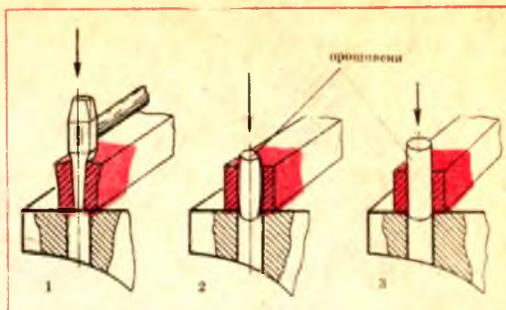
Прошивка отверстий: 1 — предварительная пробивка; 2 — прошивка бочкообразным прошивком; 3 — калибровка
